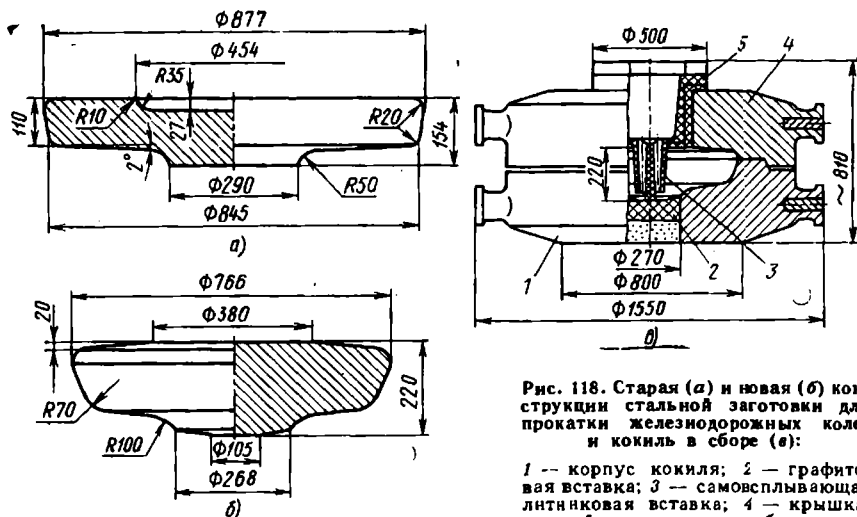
Старая (а) и новая (б) конструкции стальной заготовки для прокатки железнодорожных колес и кокиль в сборе (в):
